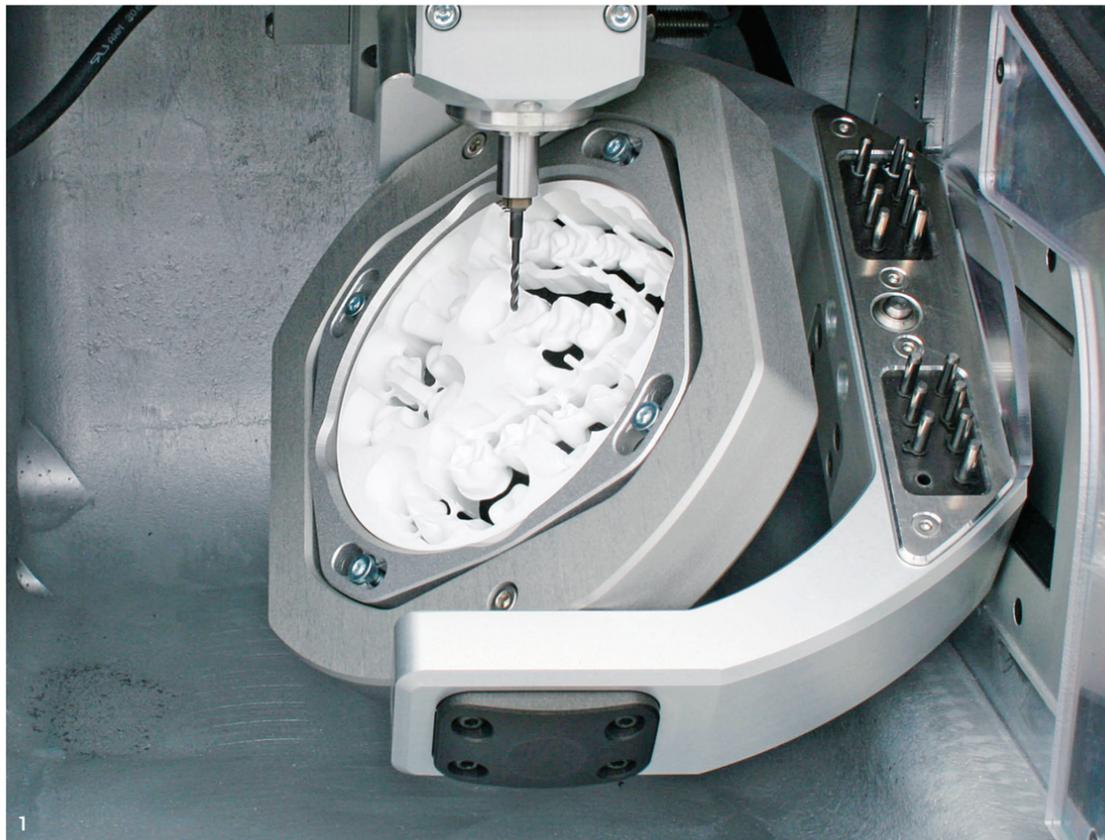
Der Innenraum einer vhf S1 bei der Bearbeitung. Mit der fünfschigen Fräsmaschine wurden die Prothesenproben für die Studie gefertigt.
